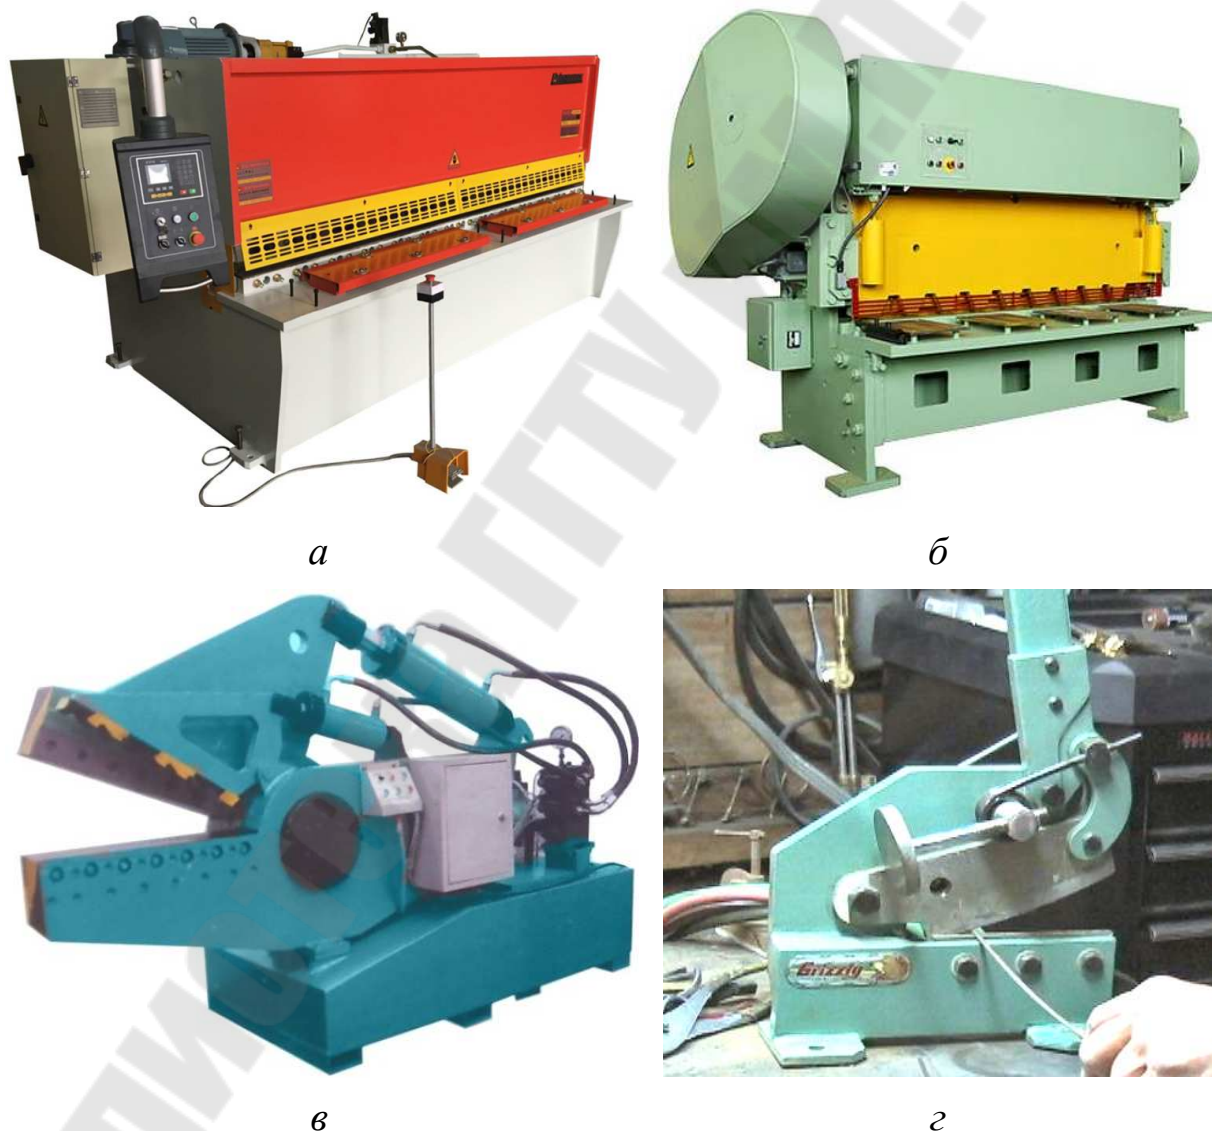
Ножницы с линейными ножами: а – гидравлические; б – кривошипные; в – аллигаторные; г – ручные
